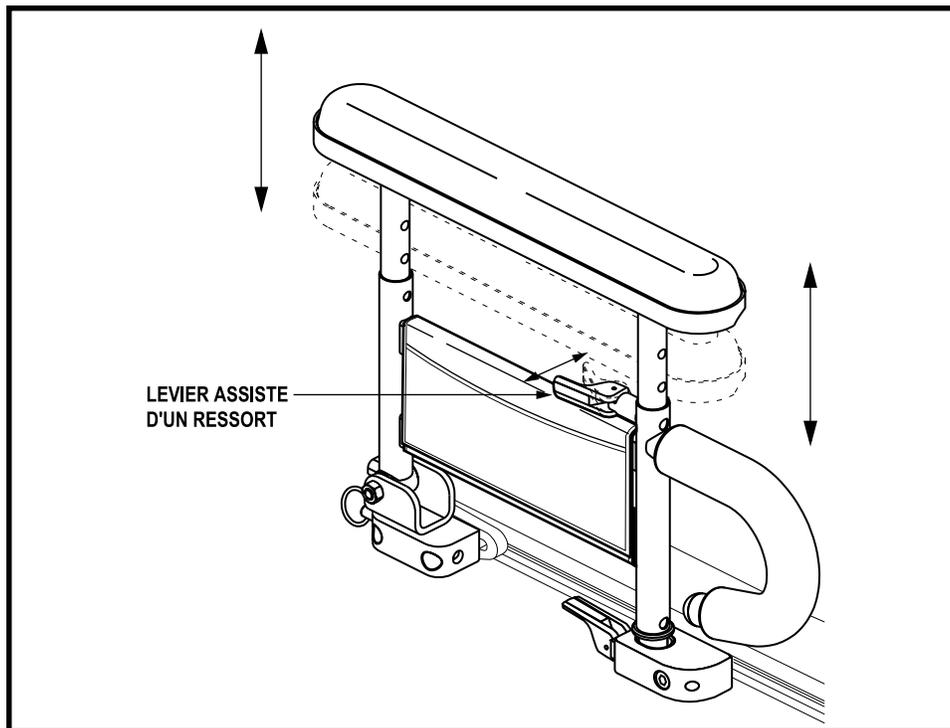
Réglage hauteur accoudoir relevable à deux montants
